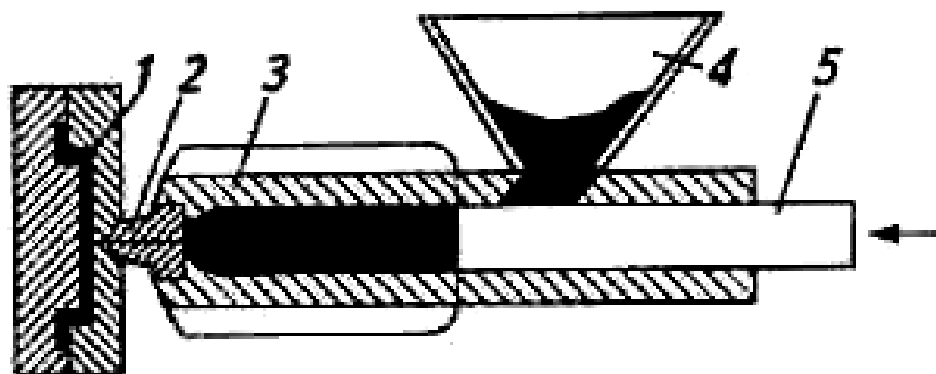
Схема машины для литья под давлением деталей из пластмасс: 1 - пресс-форма; 2 - сопло; 3 - цилиндр; 4 - бункер; 5 - плунжер
